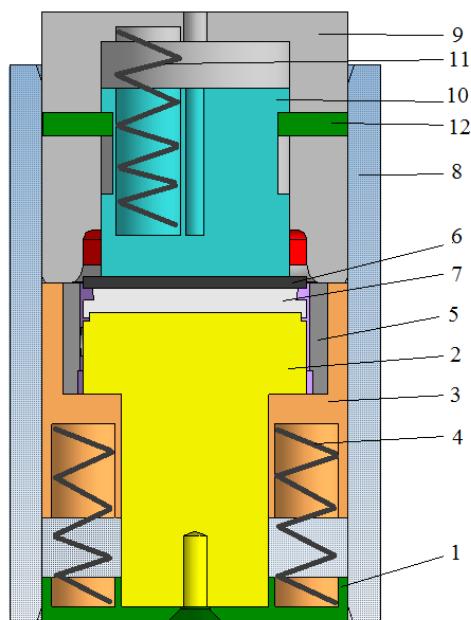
Конструкция приспособления для создания «СВМПЭ - металл»: 1 - опора; 2 - стойка; 3 - стакан; 4 - пружина стакана; 5- втулка центрирующая; 6 - диск СВМПЭ; 7- металлическая подложка; 8- гильза; 9 - матрица; 10 –прижим; 11 - пружина прижима; 12 – сухари.
